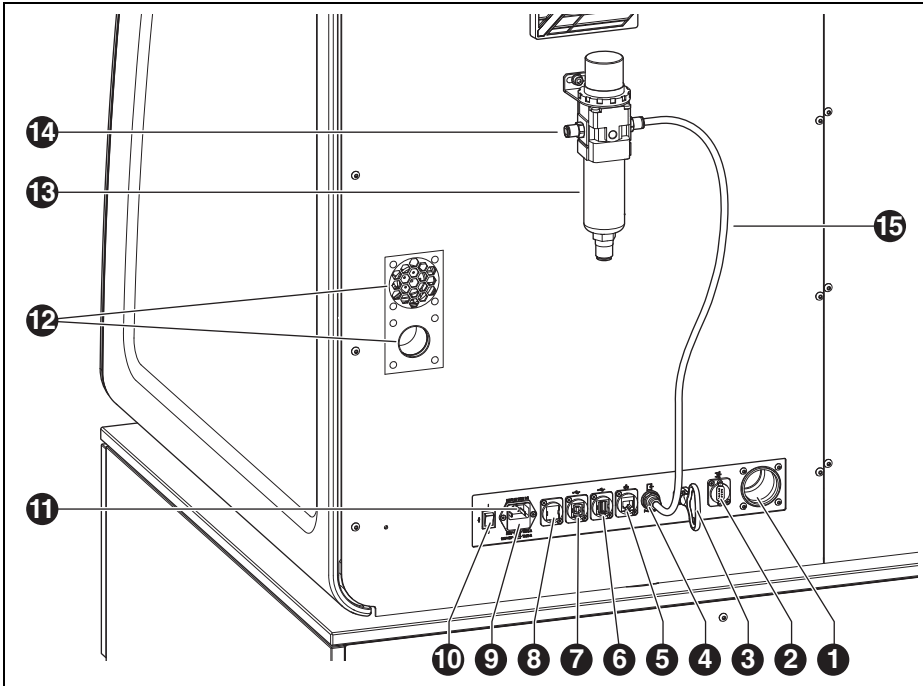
Visão geral do lado de trás do sistema de fresagem
